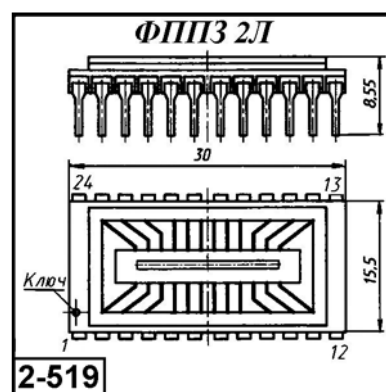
Внешний вид и габаритные размеры ФППЗ 2Л
